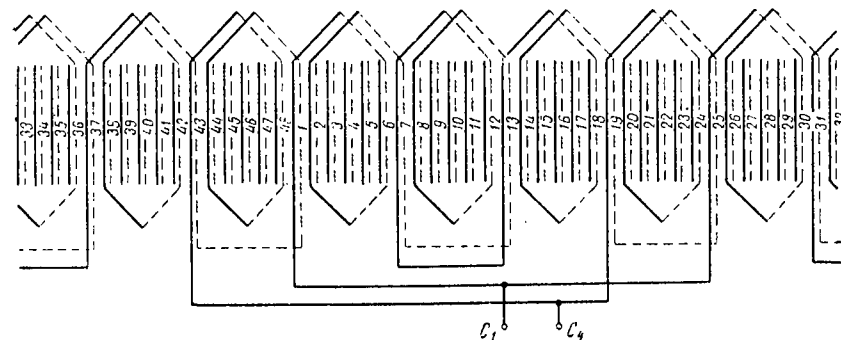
Схема двухслойной обмотки с двумя параллельными ветвями
